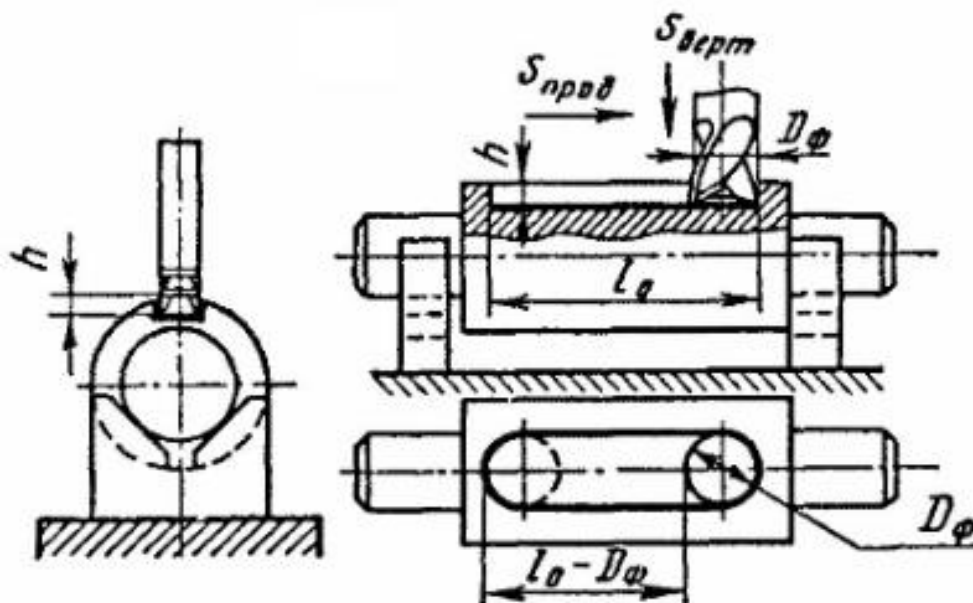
Фрезерование шпоночного паза концевой фрезой
